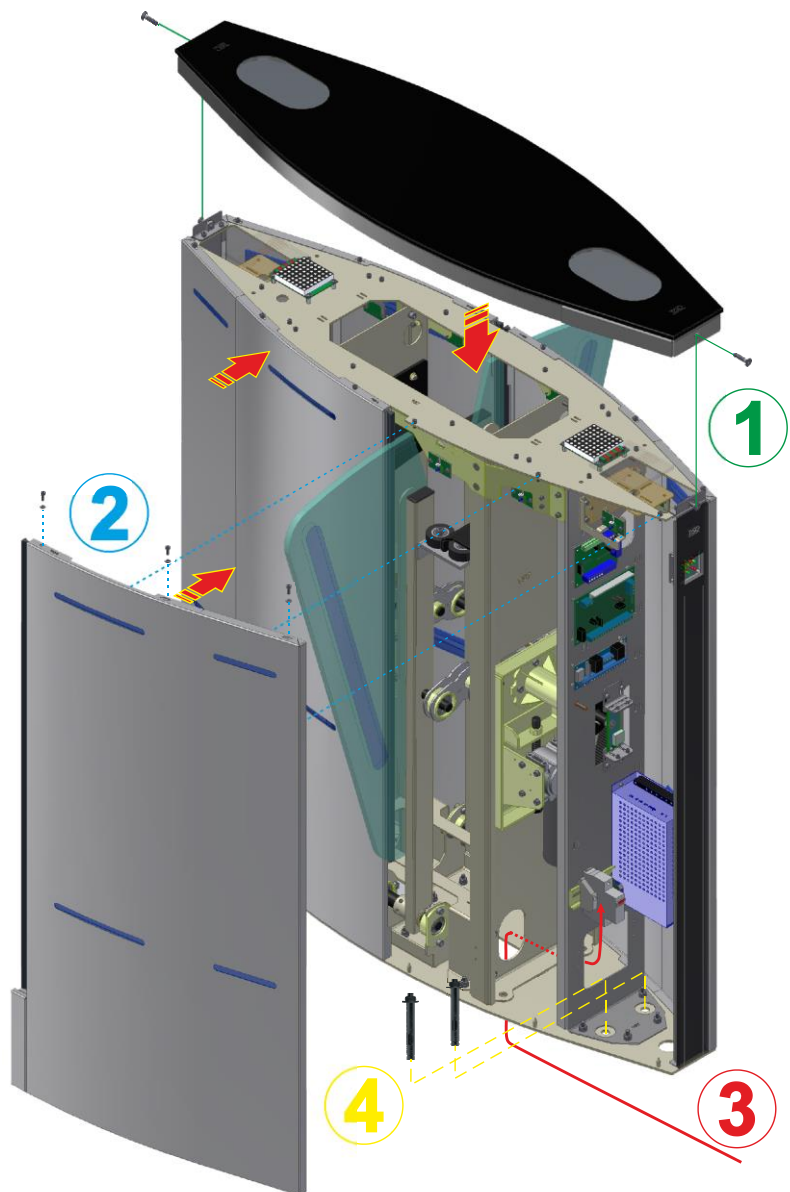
Общий вид установки тумбы турникета «SPEEDBLADE»
